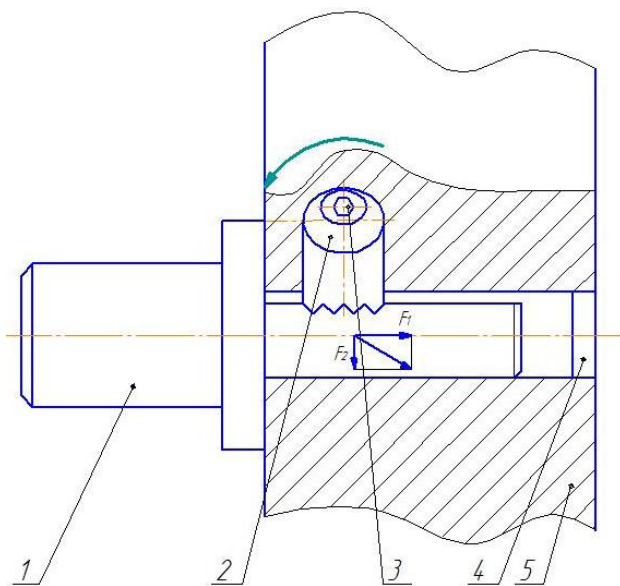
Крепление инструмента в револьверной головке: 1 – инструмент, 2 – зубчатое зацепление эксцентрика, 3 – винт, 4 – зажим, 5 – револьверная головка
